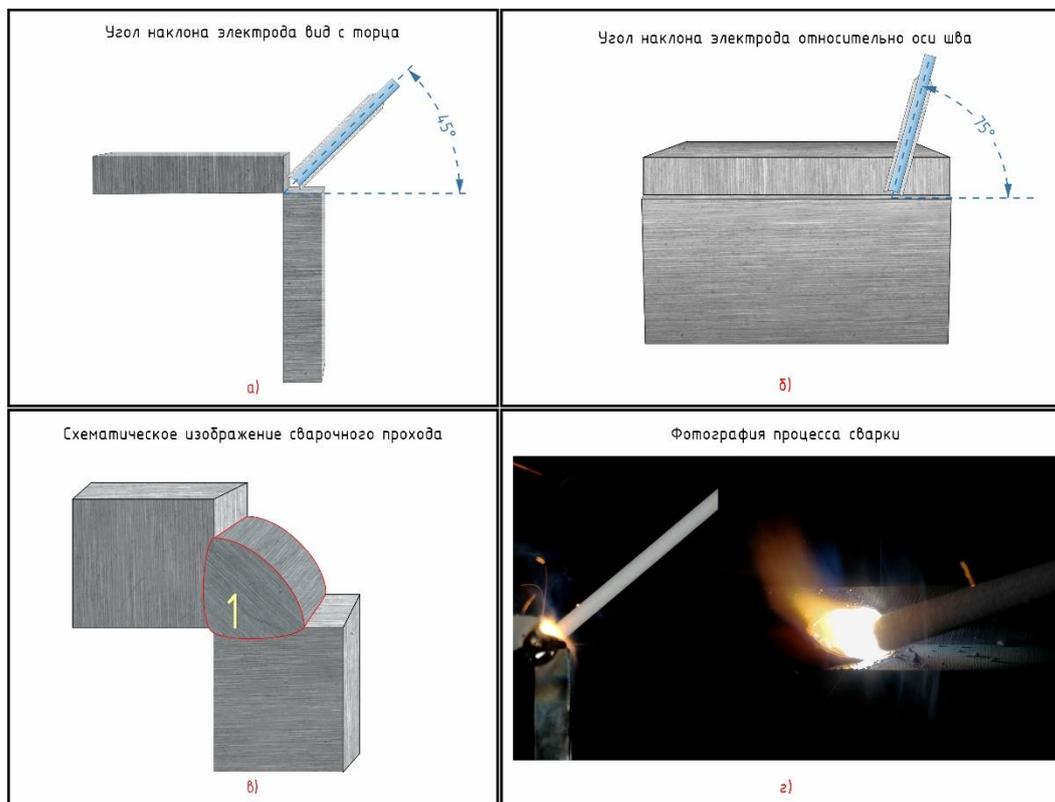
Углы наклона электрода при сварке корневого прохода соединения У4 в положении РВ
